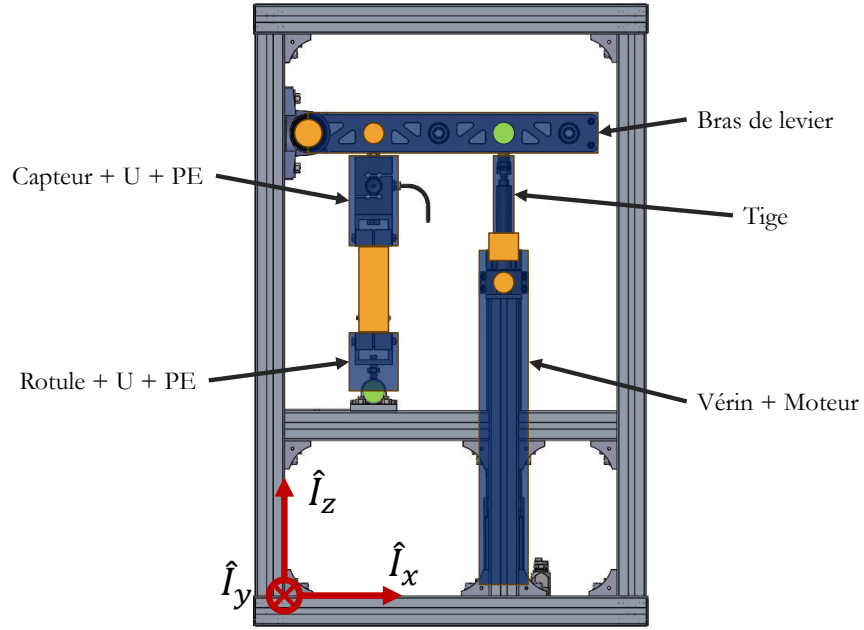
Assemblage multi-corps du démonstrateur
